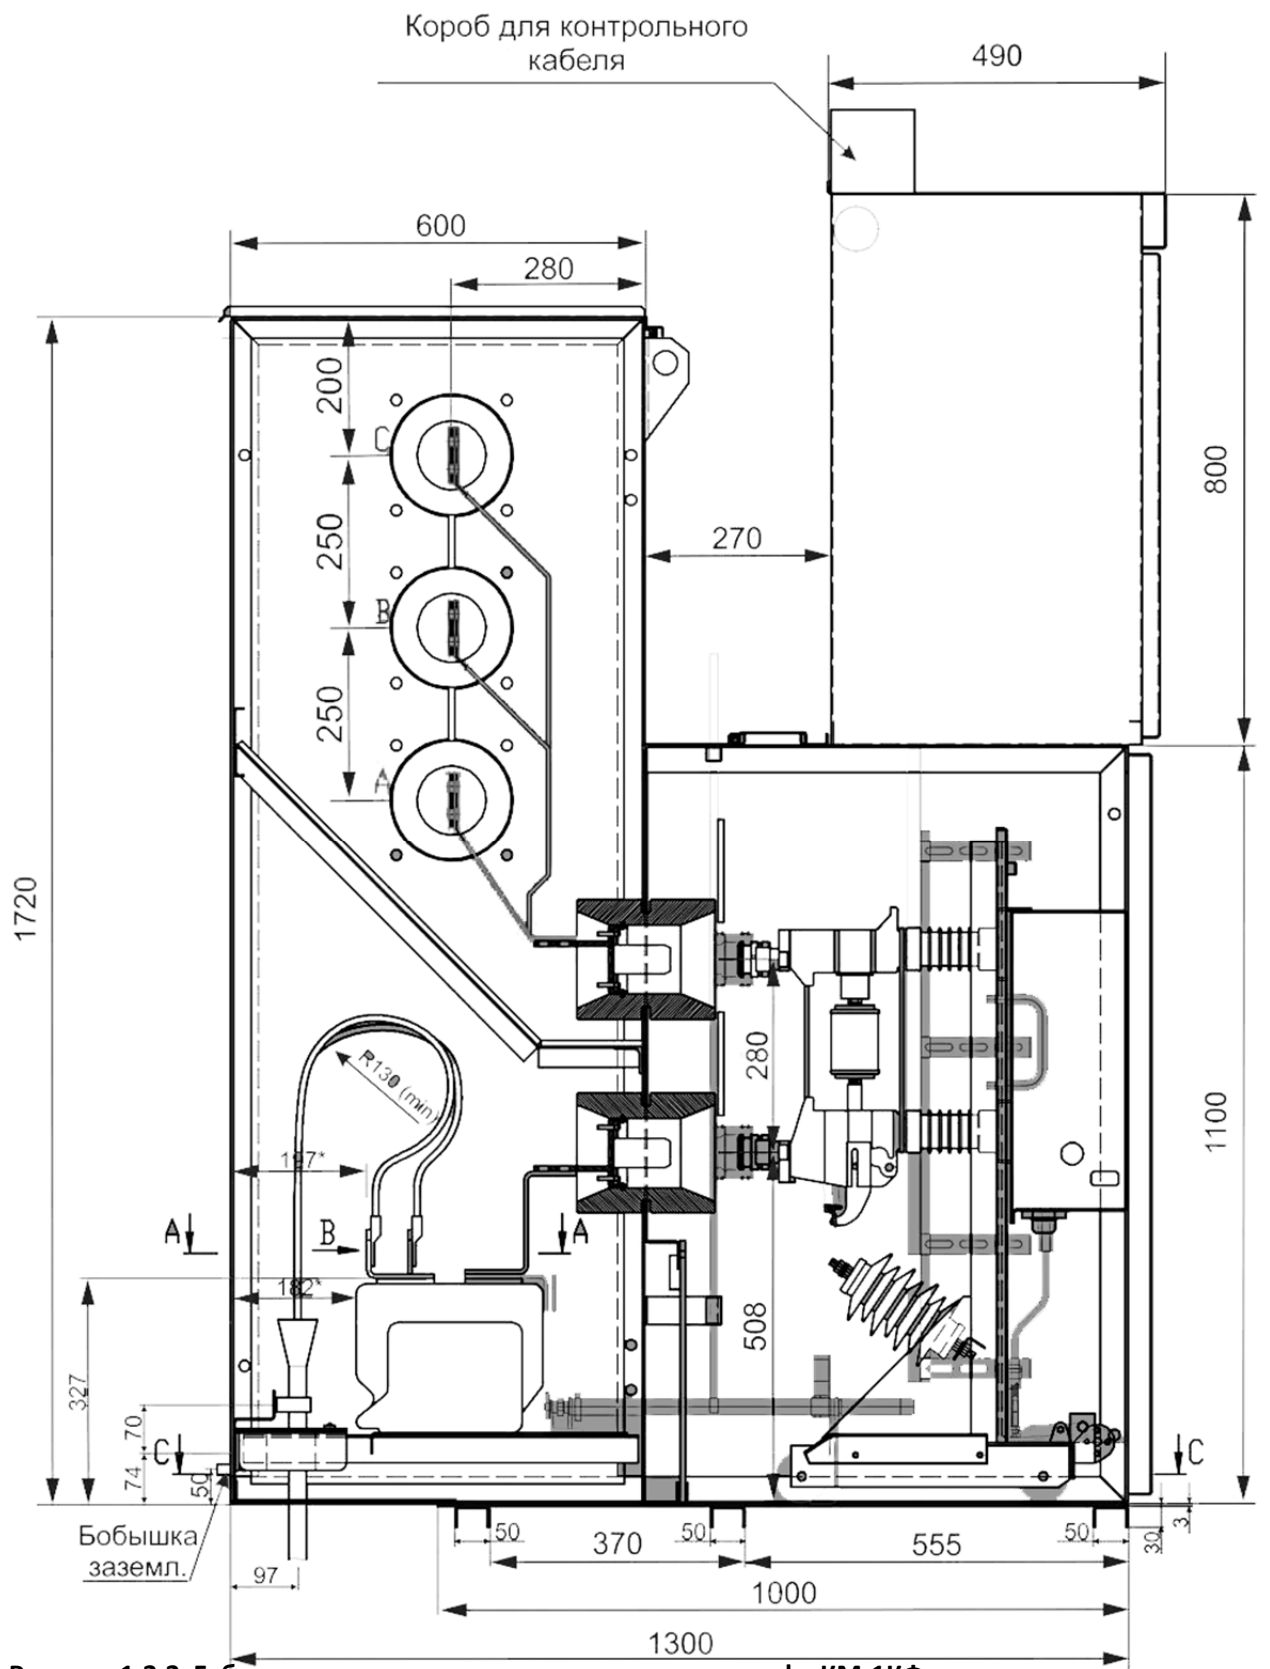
Габаритно-присоединительные размеры шкафа КМ-1КФ с вакуумным выключателем
